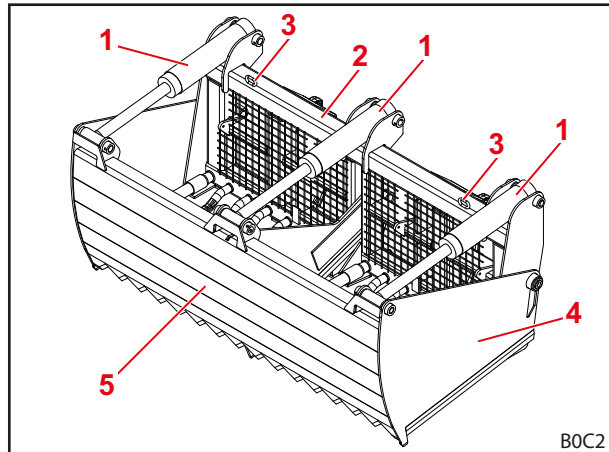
Opbygning af ensilageskærer med 3 hydraulikcylindere
